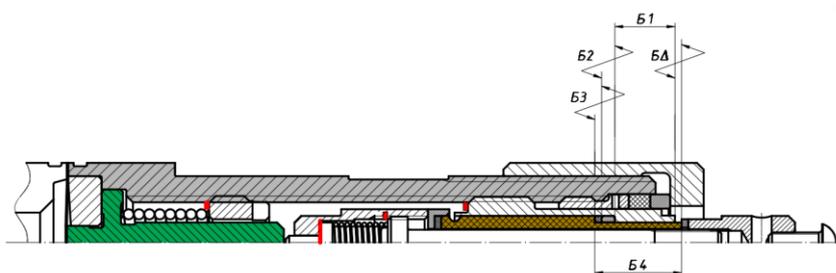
Схема размерной цепи Б, обеспечивающей при сборке СП достижение точности выступа изолятора за пределы его корпуса
